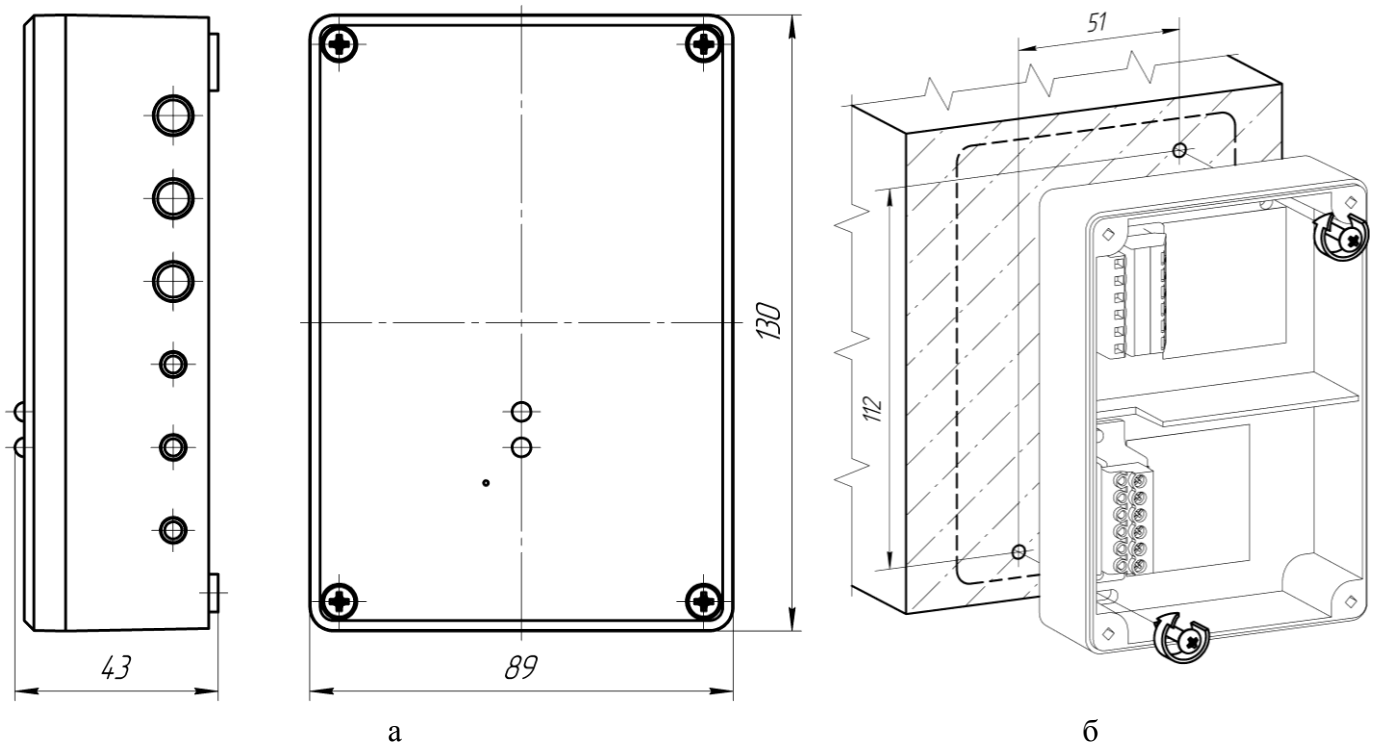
Внешний вид и габаритные размеры (а), установочные размеры (б) блока, размеры в мм.
